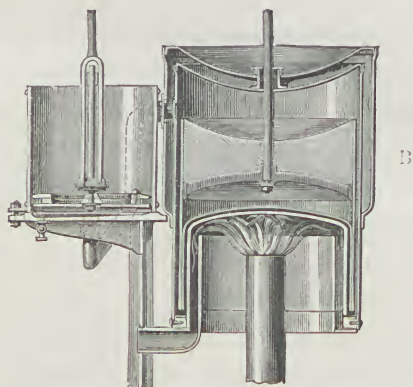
Sección de los cilindros de la máquina Laubereau
